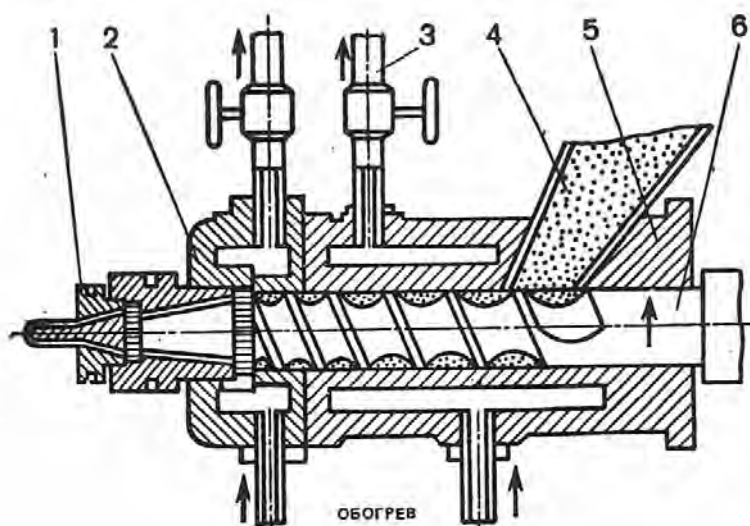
Схема экструдера: 1 - мундштук; 2 - сопло; 3 - труба для горячей воды или пара; 4 - бункер; 5 - рабочий цилиндр; 6 - шнек.
